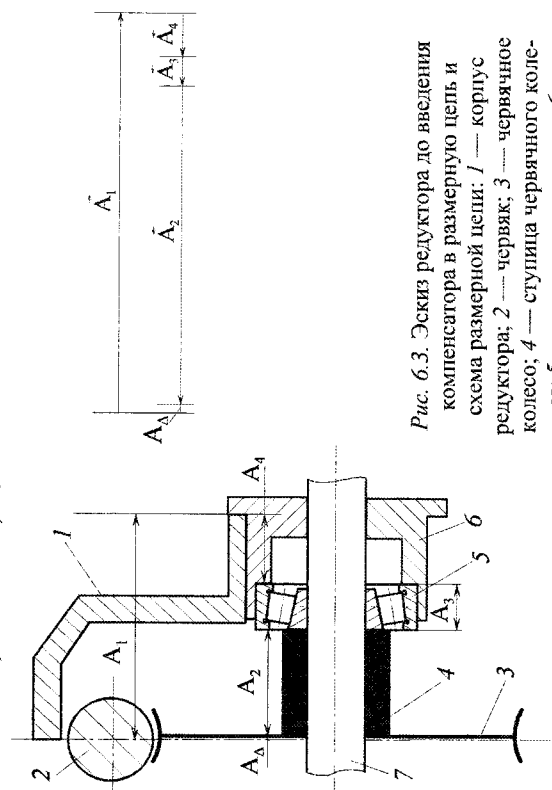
Эскиз редуктора до введения компенсатора в размерную цепь и схема размерной цепи: 1 — корпус редуктора; 2 — червяк; 3 — червячное колесо; 4 — ступица червячного колеса; 5 — подшипник качения; 6 — крышка подшипника качения; 7 — вал червячного колеса
